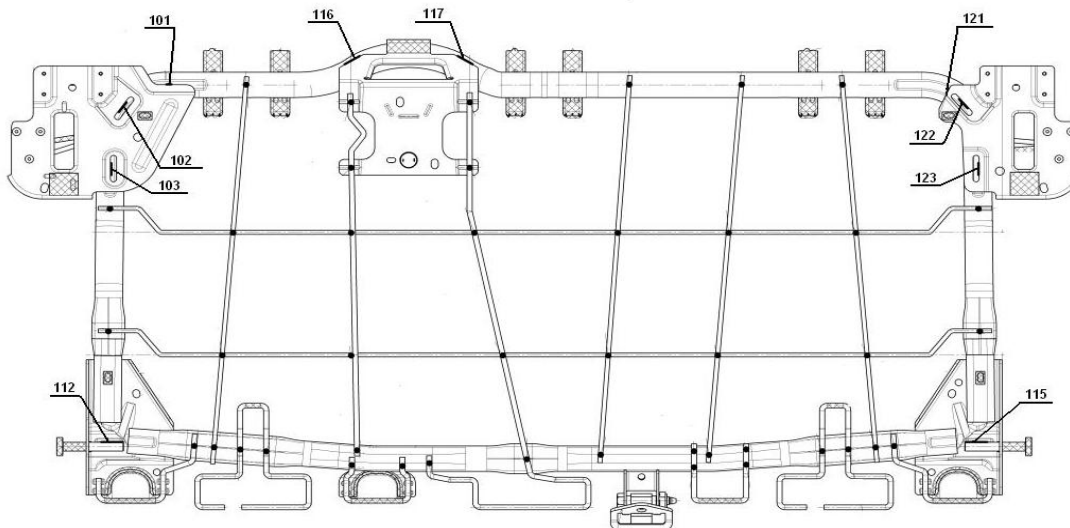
Localização dos cordões de soldadura - Visão traseira
